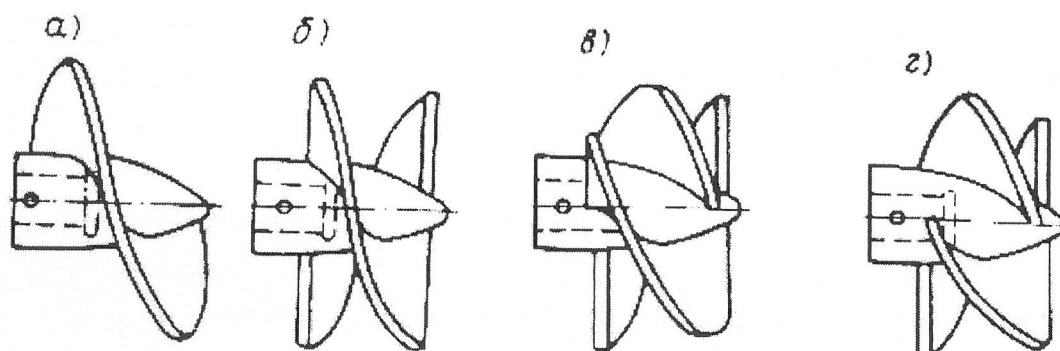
Конструкції пресуючи лопатей шнекового вала
